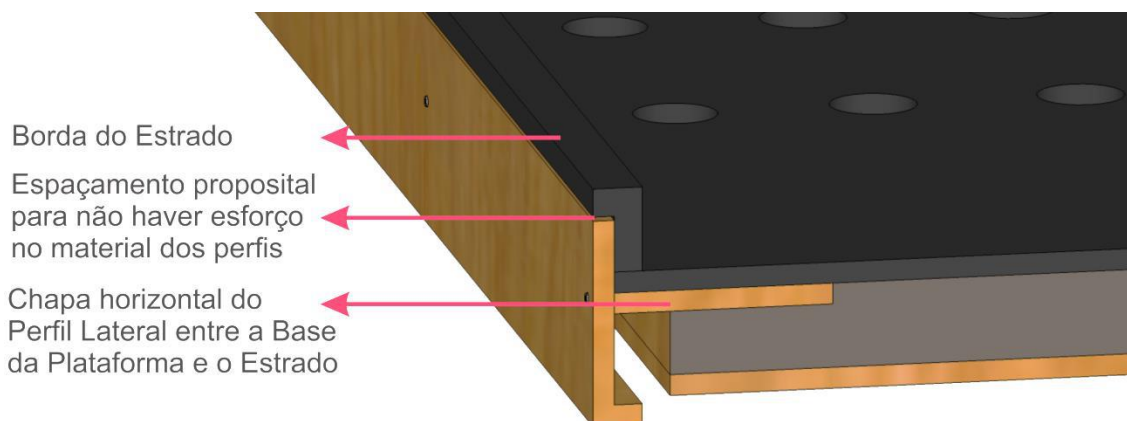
Detalhe encaixe da estrutura do *Conjunto Cama* (Fonte: elaboração própria).
